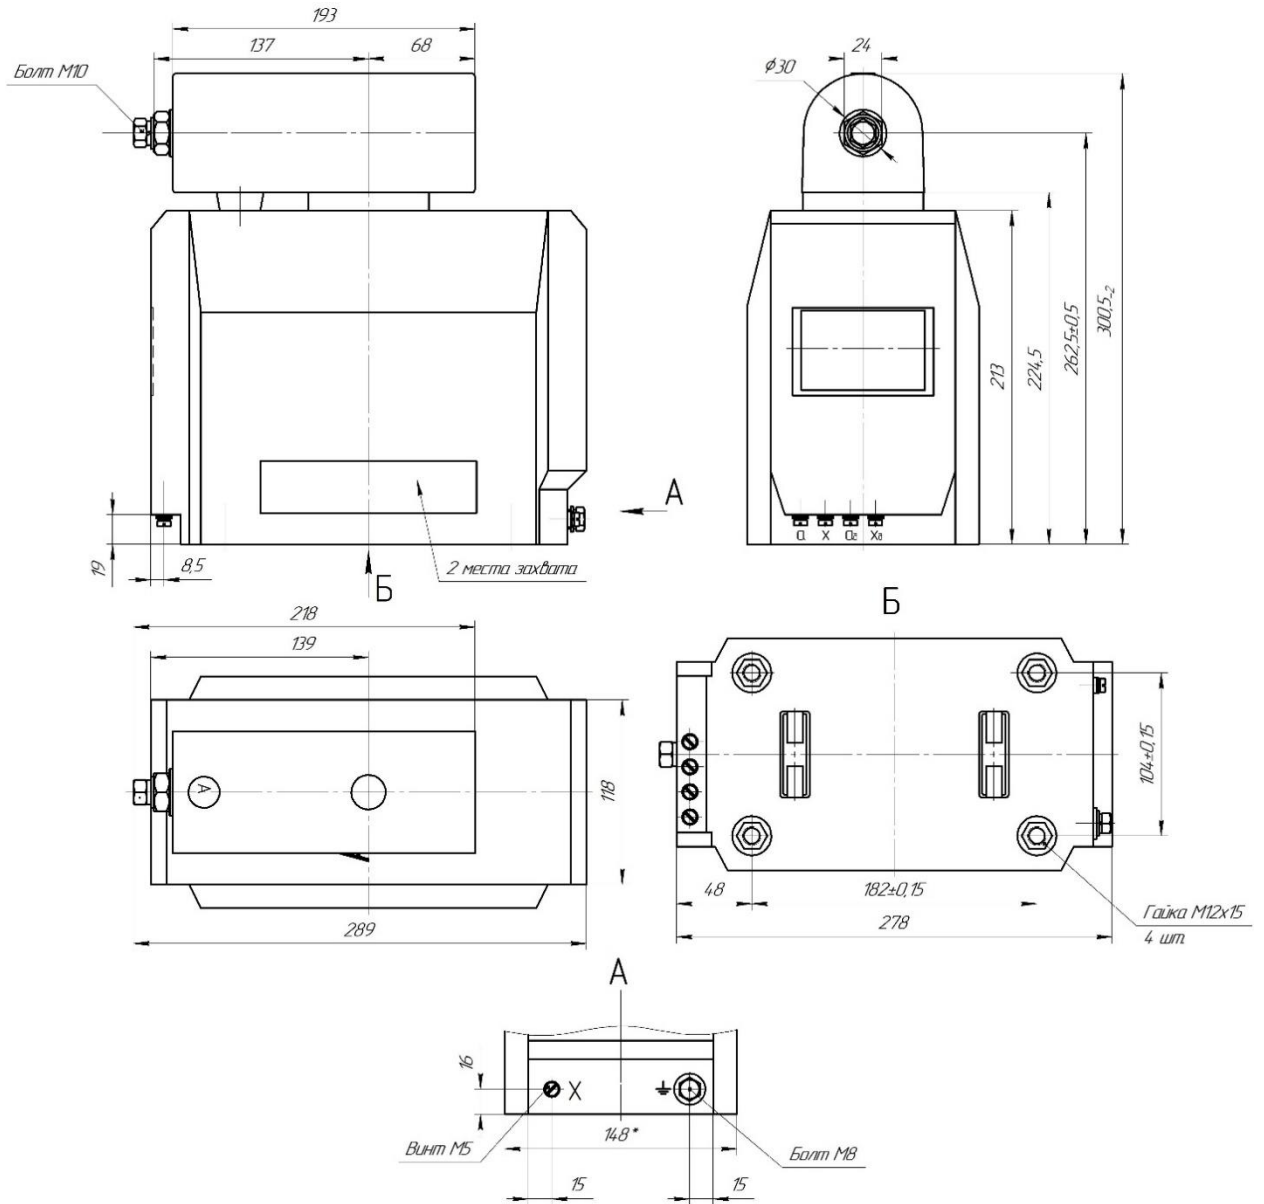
Габаритные, установочные и присоединительные размеры трансформаторов напряжения ЗНОЛ-СЭЦ-6-10 и ЗНОЛ-СЭЦ-10-10
